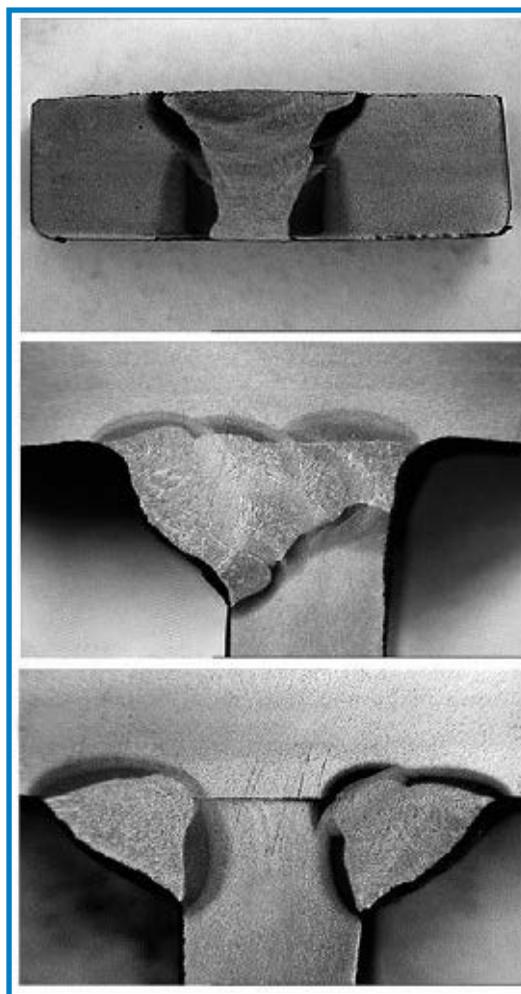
Макрошлифы сварных соединений, выполненные порошковой проволокой MEGAFIL 821R диаметром 1,2 (корневые проходы) и 1,6 мм в углекислом газе
